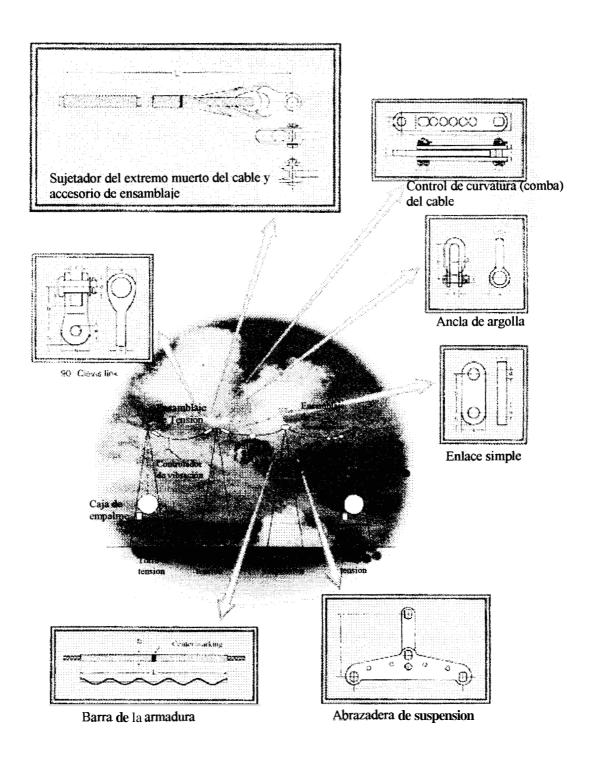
Accesorios para tendido de fibra opgw por tension o por suspension
